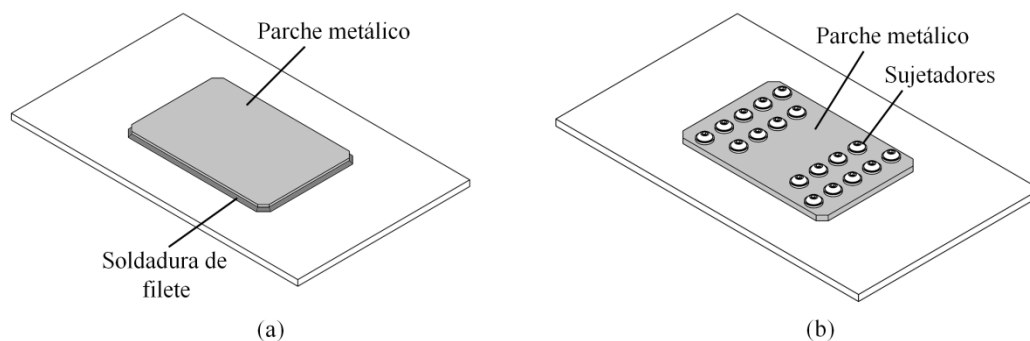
Arreglos típicos de parches metálicos para estructuras aeronáuticas o geometrías planas. (a) Parche metálico fijado con soldadura de filete. (b) Parche metálico fijado con sujetadores.
